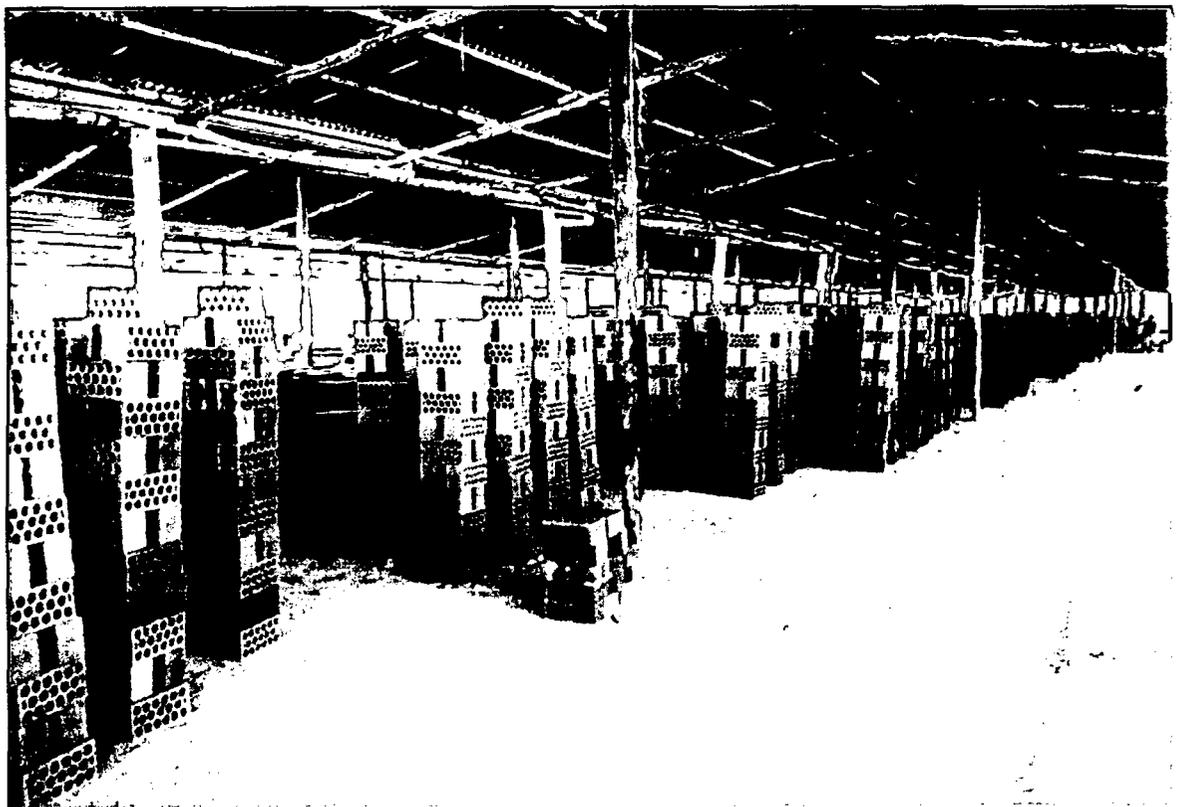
b Secadero bajo techo en la vista ladrillo kk de 18 huecos
